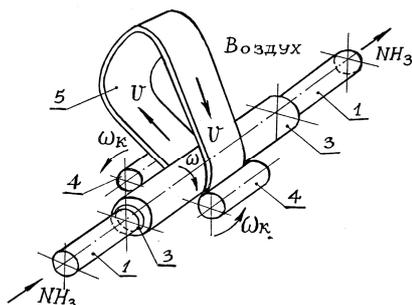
Схема ленточного динамического воздухоохлаждителя с теплопередачей через подшипниковый узел: 1 – трубопровод с хладагентом; 2 – теплопоглощающий элемент (барaban), корпус подшипникового узла; 3 – сальниковые уплотнения подшипникового узла; 4 – кинематические связи (катки); 5 – ленточный радиатор
